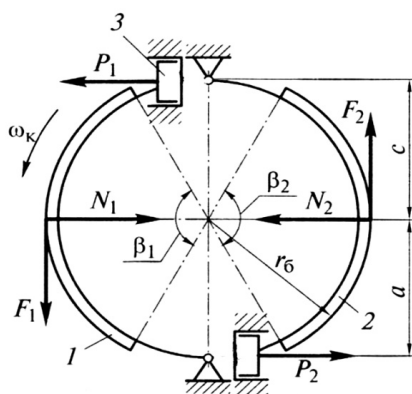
Схема барабанного тормозного механизма с гидравлическим приводом, равными приводными силами и двухсторонним расположением фиксированных опор: 1 и 2 – тормозные колодки; 3 – колесный цилиндр
